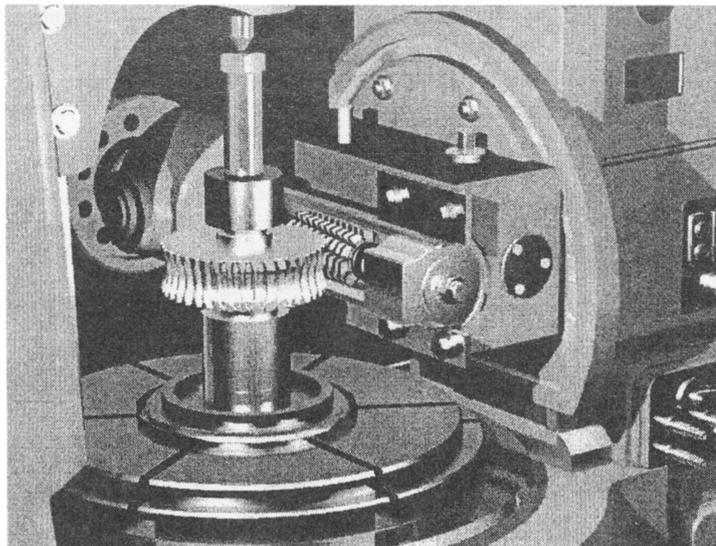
Нарезание на зубофрезерном станке червячного колеса методом радиальной подачи
